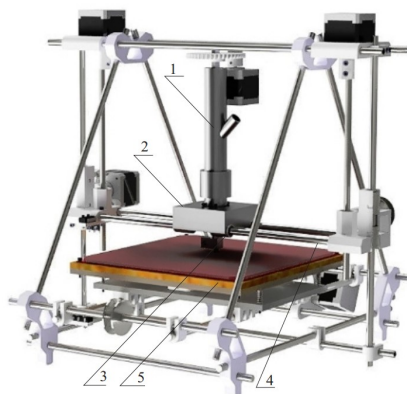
Загальний вигляд установки із пристроєм для переробки полімерних мас: 1 – екструдер; 2 – кріплення установки екструдера; 3 – підшипник прямолінійного руху; 4 – вал переміщення пристрою; 5 – робоча поверхня для охолодження вихідного матеріалу
